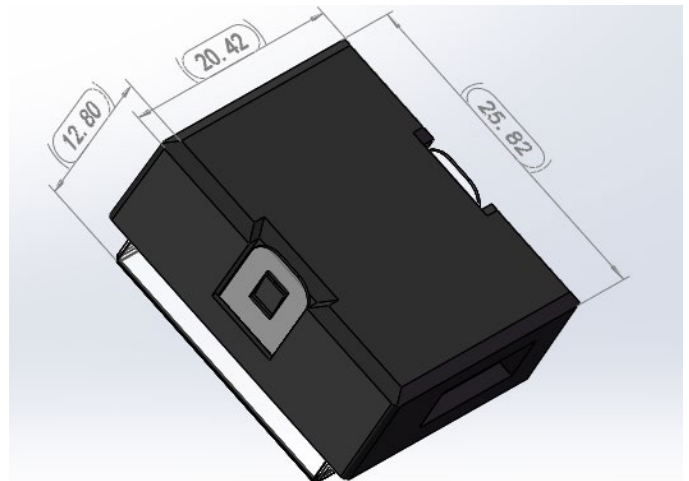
Внешний вид и габаритные размеры TOPAZ DT RS485 WSB
